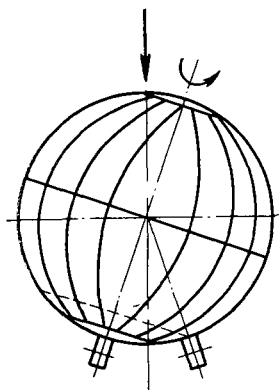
Положение сферического резервуара при сварке полюсного шва
